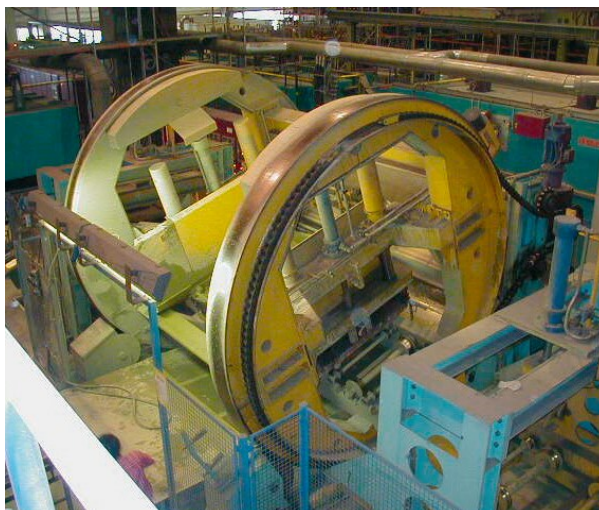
Bubnový obraceč Palmer C-Frame [6]
